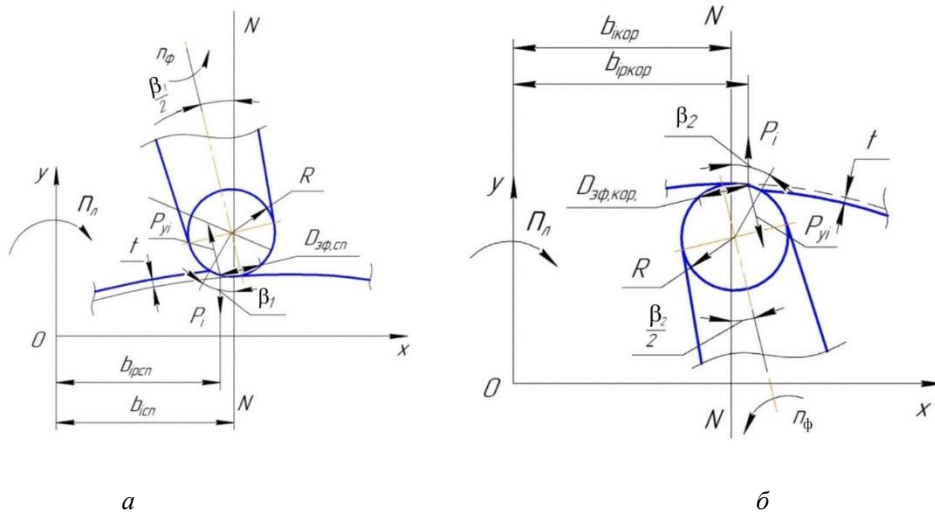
Геометрические связи в зоне контакта фрезы со сферической рабочей поверхностью спинки (а) и корыта (б) лопатки при встречном фрезеровании:  $t$  – глубина фрезерования;  $n_l, n_f$  – соответственно частоты вращения лопатки и фрезы;  $R$  – радиус сферической режущей части фрезы;  $D_{эф.сп.}, D_{эф.кор.}$  – соответственно средний эффективный диаметр режущей кромки на спинке и корыте;  $\beta_1/2, \beta_2/2$  – соответственно угол разворота оси фрезы от нормали  $N-N$  к точке фрезеруемого профиля на спинке и корыте;  $\beta_1, \beta_2$  – углы дуг (длиной  $B_{сп.}, B_{кор.}$ ) зоны контакта фрезы и лопатки;  $P_{yi}$  – нормальная составляющая силы фрезерования на среднем эффективном диаметре режущей кромки;  $b_{i\text{ сп.}}, b_{i\text{ кор.}}$  – плечи нормалей  $N-N$  к точкам фрезеруемого профиля, согласно чертежу лопатки;  $b_{ip\text{ сп.}}, b_{ip\text{ кор.}}$  – текущие плечи приложения проекций  $P_{yi}$  нормальных составляющих силы фрезерования  $P_i$  на ось  $Y$
